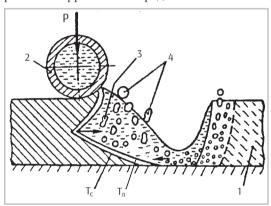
Схема высокотемпературной прокатки в процессе сварки: 1 — свариваемое изделие; 2 — ролик; 3 — сварочная ванна; 4 — пузырьки газа; Р — давление ролика; T_c — зона солидуса; T_n — зона ликвидуса
